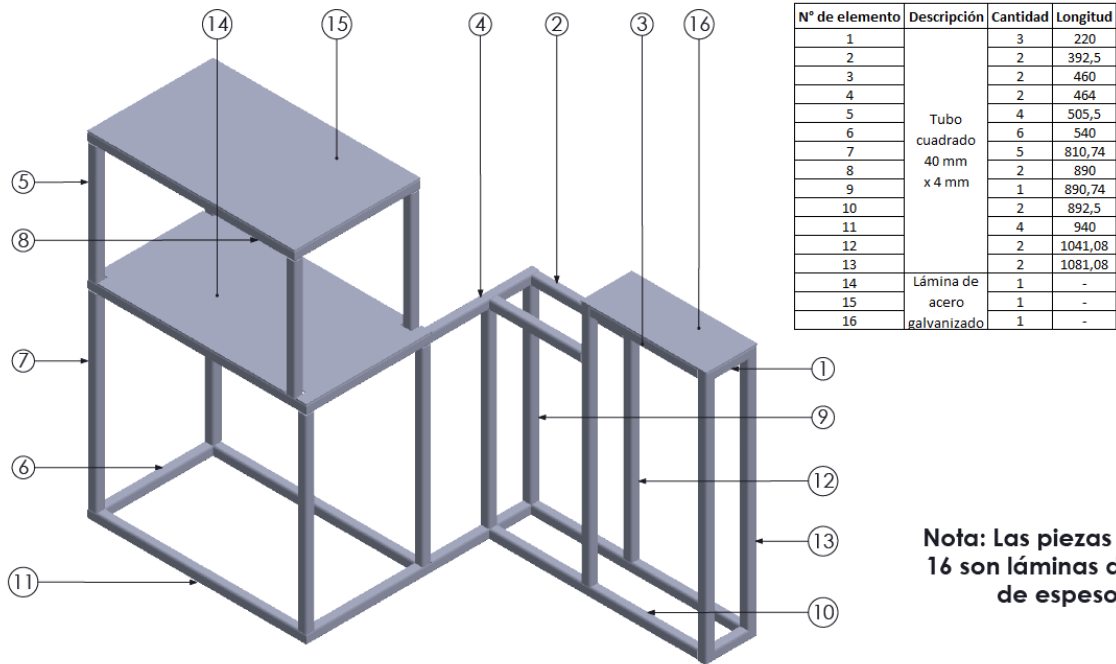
Detalles de ubicación de las uniones y paneles de cerramiento de la estructura
